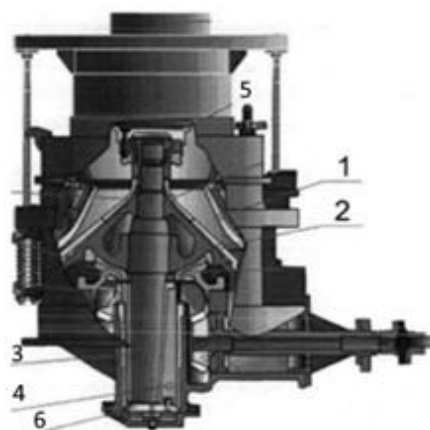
Схема устройства конусной дробильной установки:
